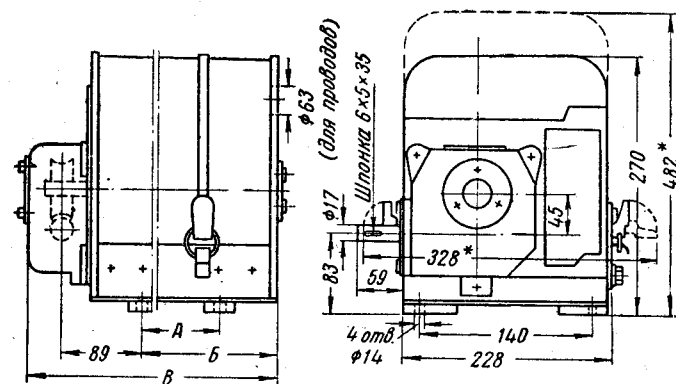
Командоаппараты КА-4028, КА-4048 и КА-4058 (с редуктором); \* — габаритные размеры с открытыми замками и снятым кожухом.
